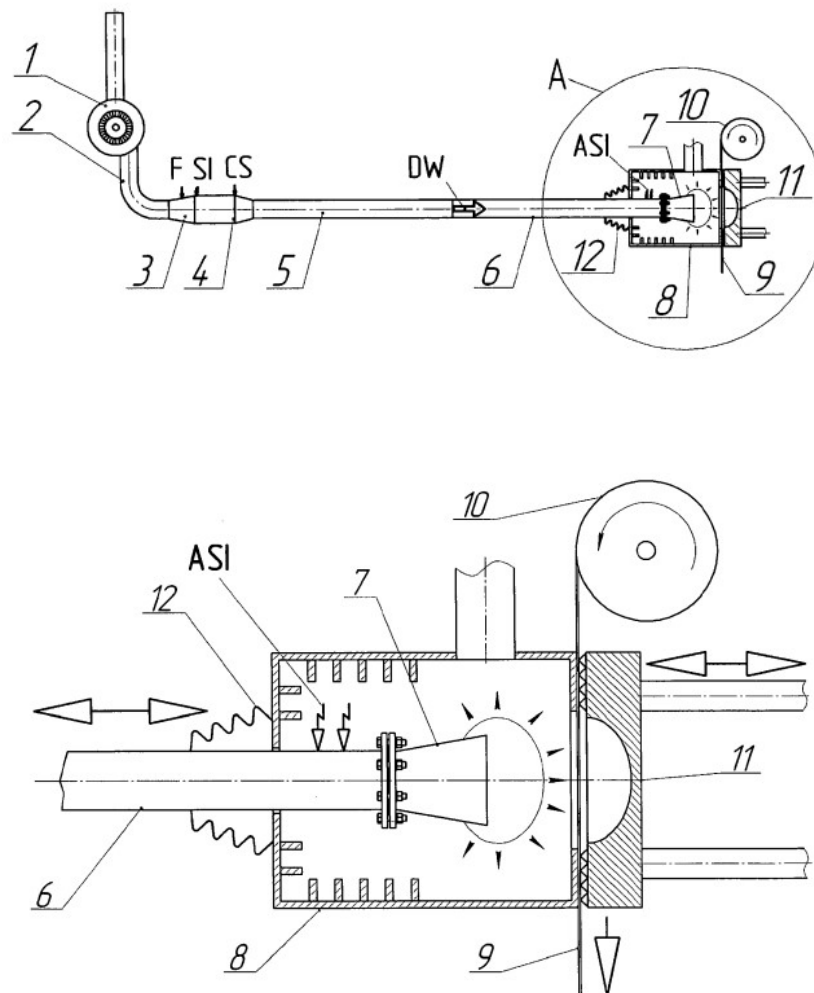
11 – Схема пристрою для багатоімпульсного детонаційного штампування [38]: 1 - ємність з окиснювальним газом; 2 - магістраль подачі окисного газу; 3 - змішувальний пристрій зі зворотним клапаном; 4 - камера згоряння; 5 - прискорювач полум'я; 6 - детонаційна труба; 7 - вихідний насадок; 8 - вентиляований шумопоглинальний контейнер; 9 - заготовка; 10 - механізм автоматичної зміни заготовки; 11 - змінна матриця з фіксатором; 12 - сильфон;
